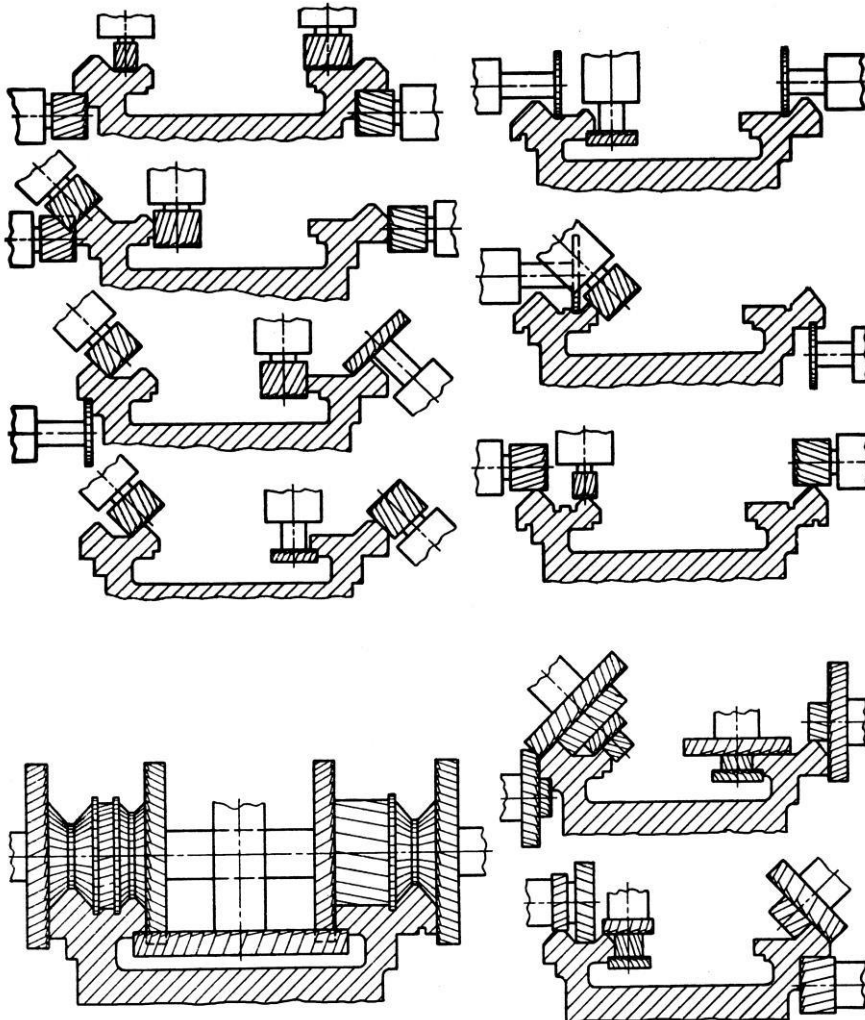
Способи фрезерування прямолінійних поверхонь
